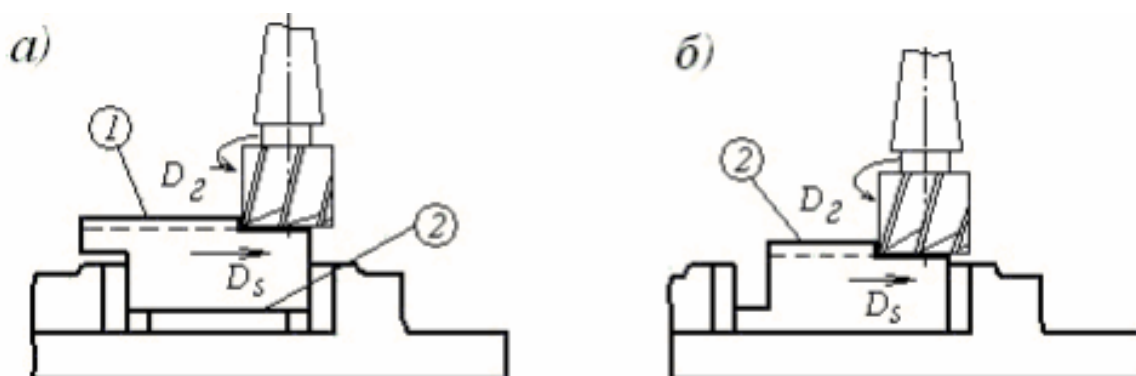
Эскизы выполнения фрезерной операции за два установка
